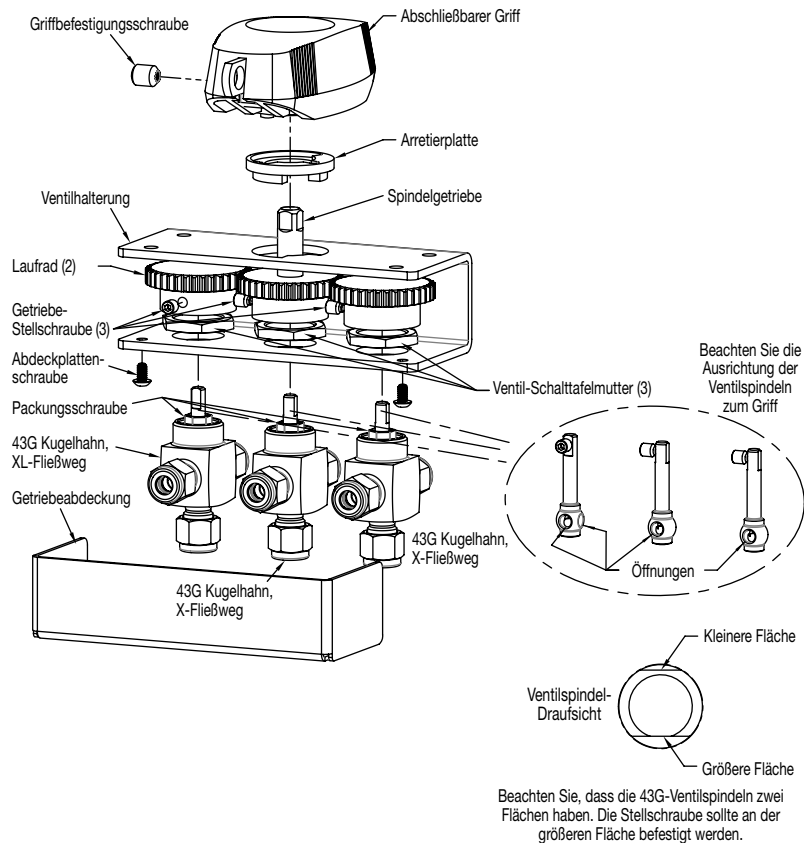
3-Ventil-GSM-Baugruppe Explosionsdarstellung
